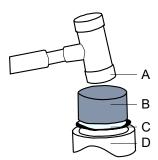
Hülse mit leichten Hammerschlägen auf die Welle treiben A - Hammer, B - Montagehülse, C - Wellenschutzhülse, D - Welle
